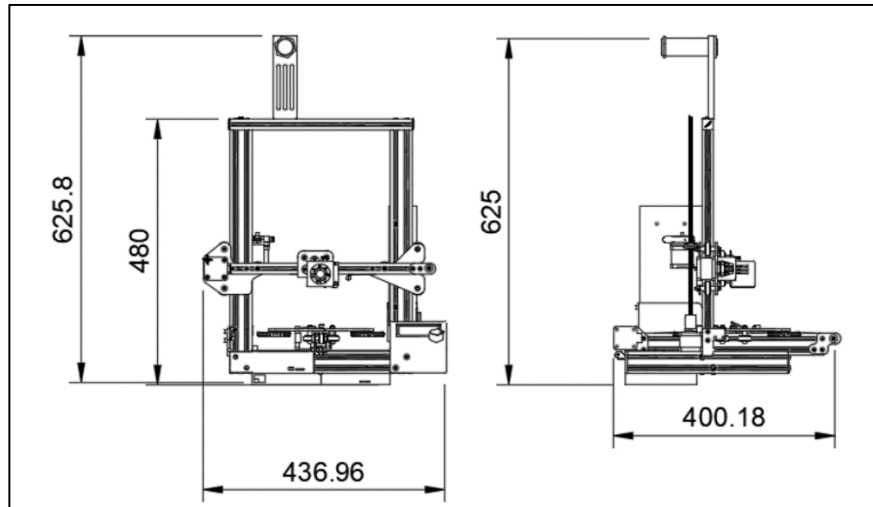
Dimensiones de impresora 3D Creality Ender 3.
